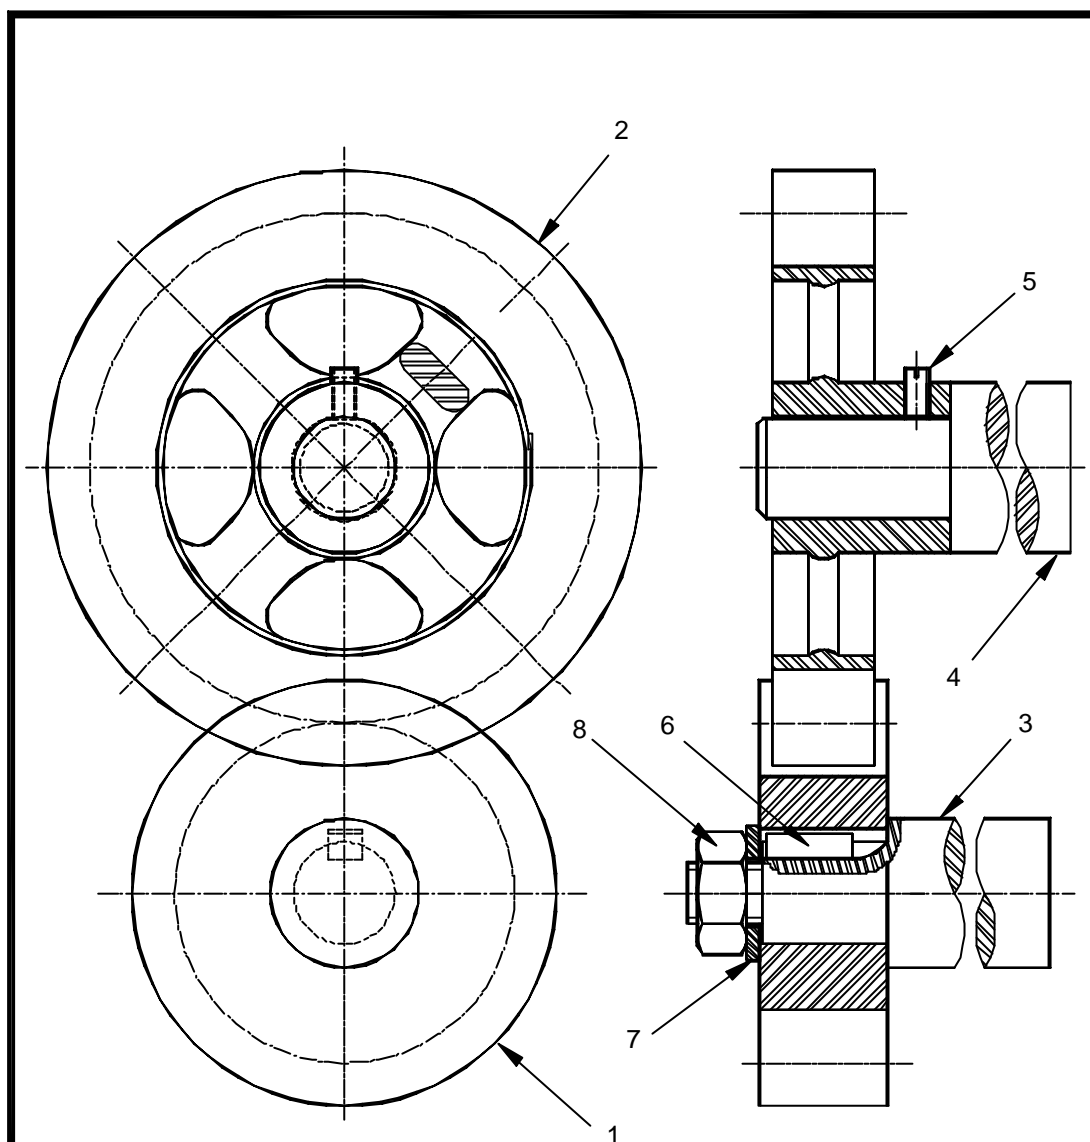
Elementos da engrenagem cilíndrica de dentes retos
